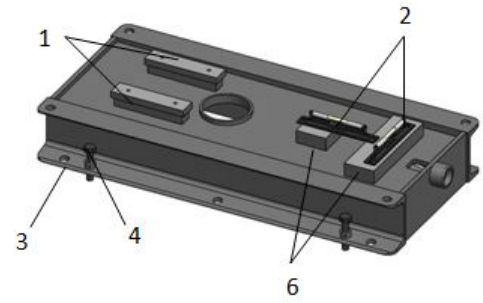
Nivelación de la placa base-cojinetes de la bomba
